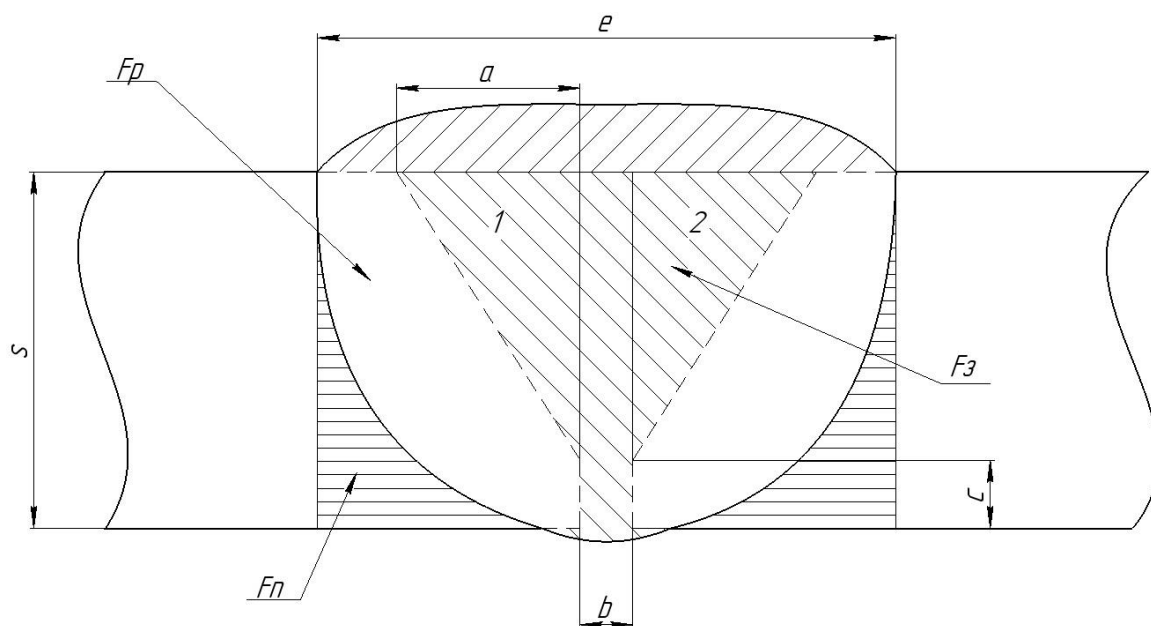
Схема для определения режимов механизированной сварки в защитных газах со скосом двух кромок
